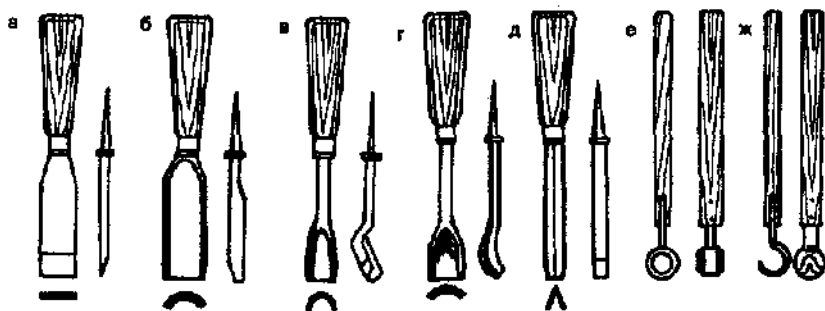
Инструменты для долбления, резания древесины и обработки криволинейных поверхностей: а — стамеска прямая; б — стамеска полукруглая (желобчатая); в — стамеска-царазик; г — стамеска-клюкарза; д — стамеска-уголок; е — ложечный резец-кольцо; ж — ложечный резец-крючок
